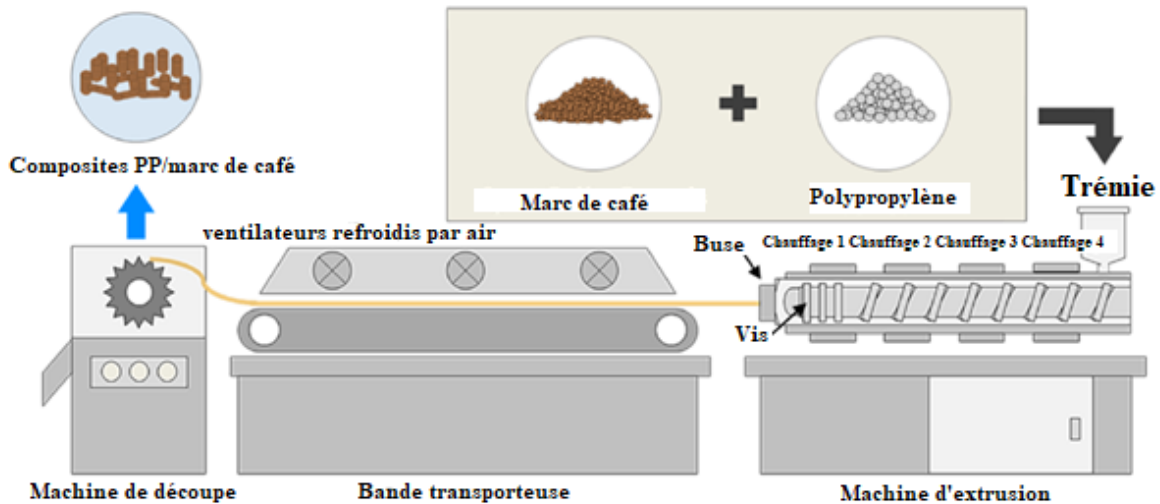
Schéma de la procédure de fabrication par la méthode de moulage par extrusion [51].
